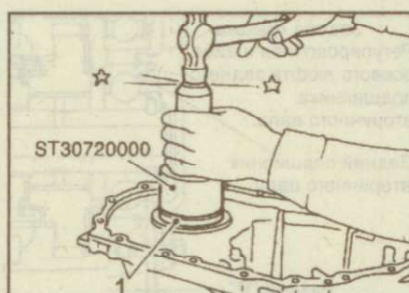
Установка наружного кольца (1) подшипника дифференциала
